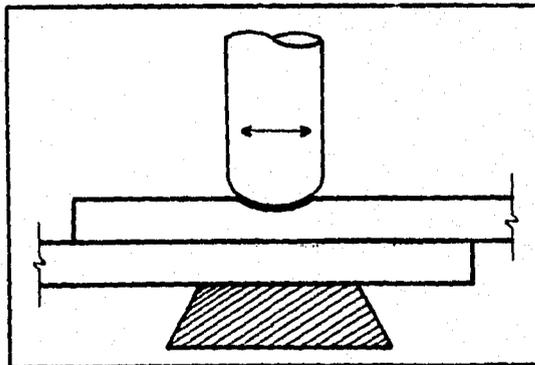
DETALLE DEL PROCESO DE SOLDADURA USW.
